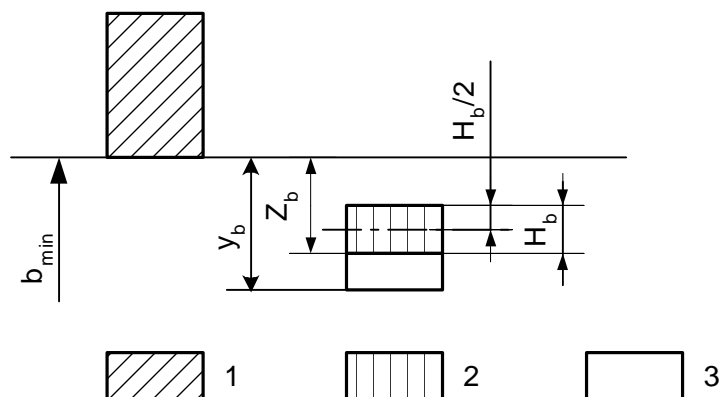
Схема расположения полей допусков диаметров  $d_k$  и  $D_k$  калибров-пробок (1 – поле допуска центрирующего диаметра  $d$  или  $D$  втулки; 2 - поле допуска на изготовление калибра-пробки; 3 - поле износа калибра-пробки)
